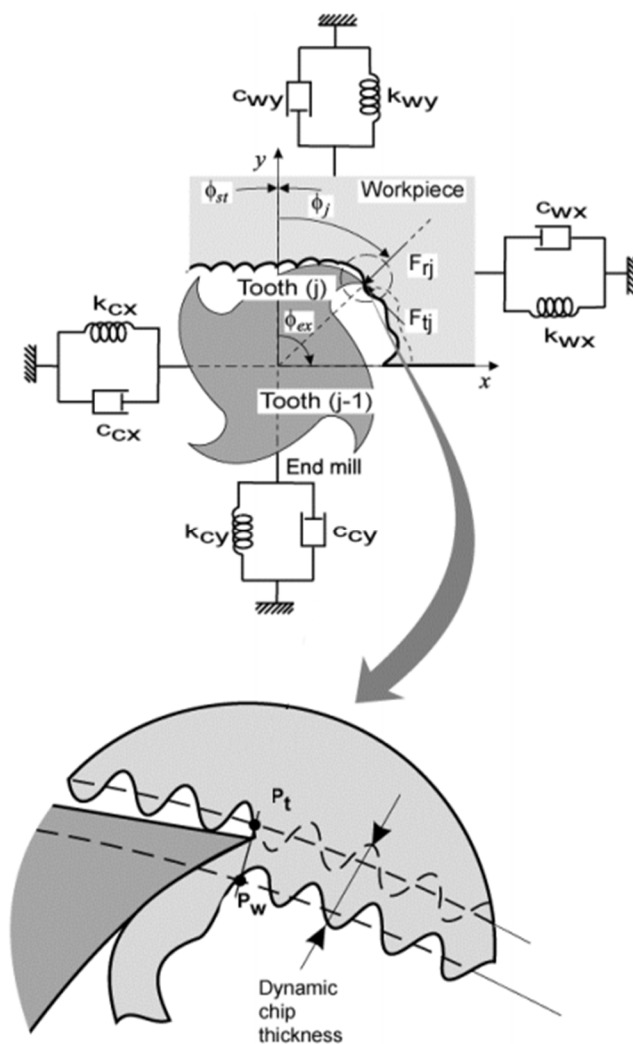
Модель обробної системи торцевого фрезерування з урахуванням динамічної системи столу [36]
